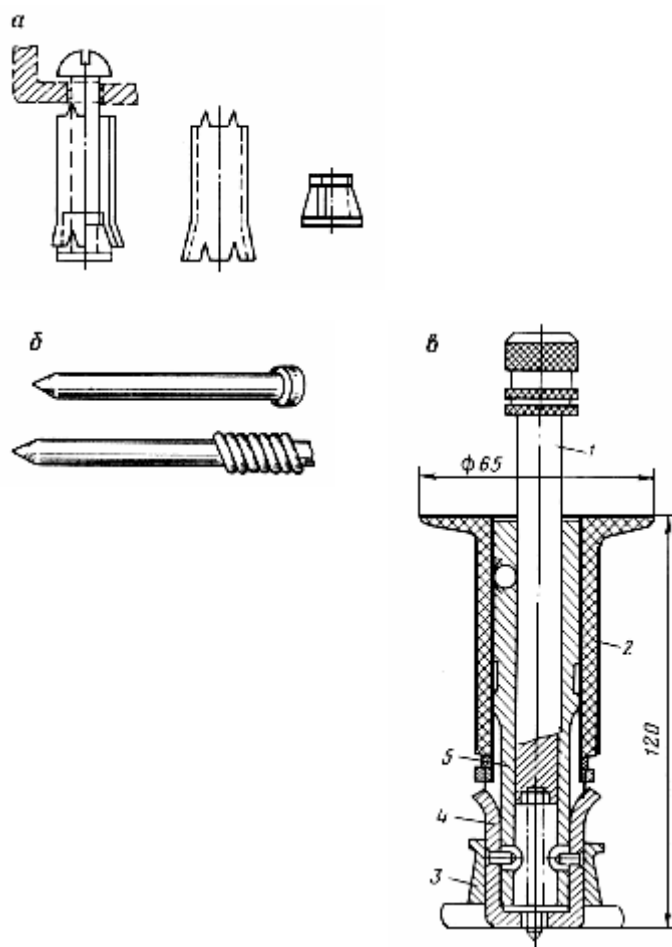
Закрепы для крепления кабелей и их конструкций:
